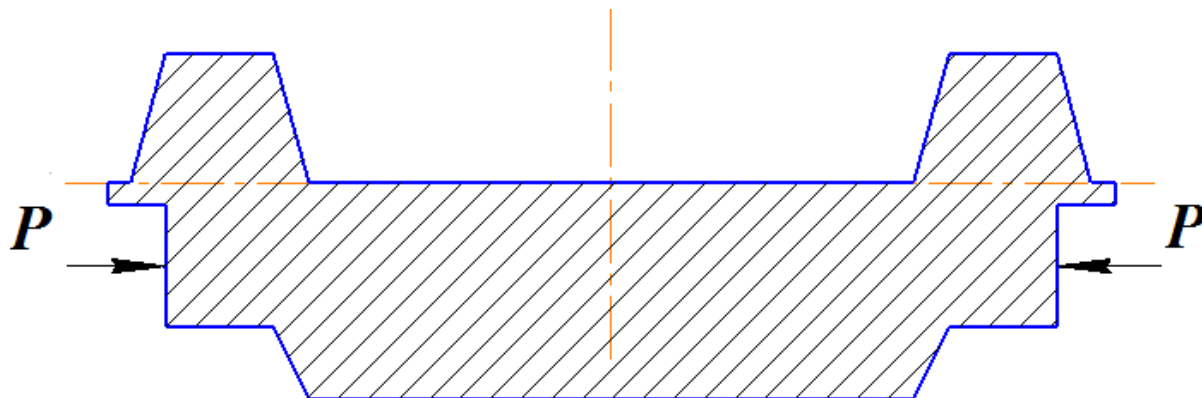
Схема дії сил, що діють на деталь у процесі її обробки
